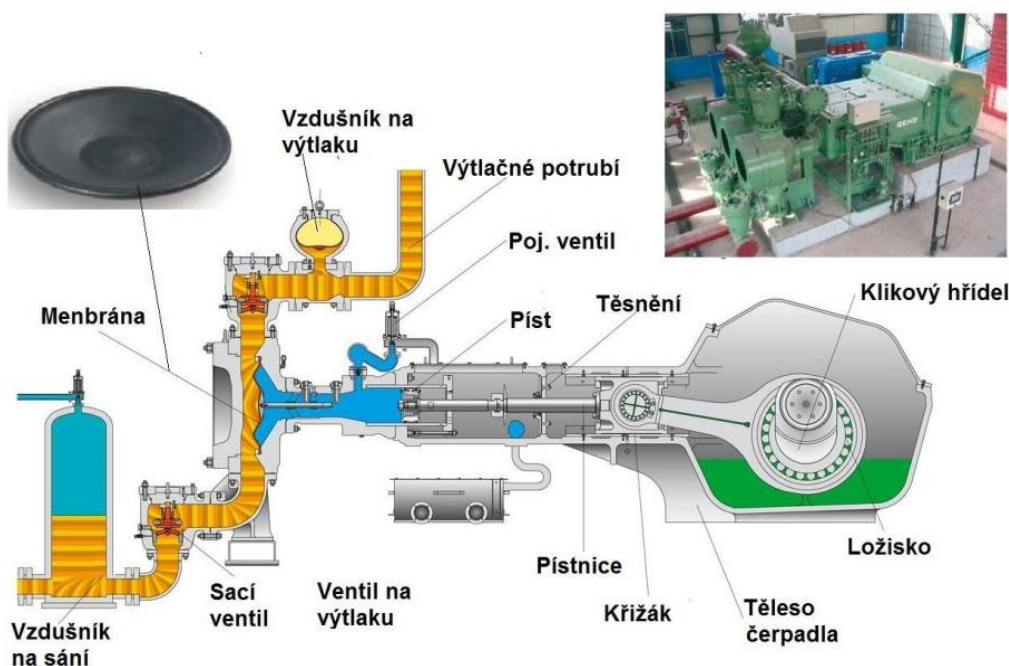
Ukázka provedení ventilů, pístů a hydraulických válec - [12]
